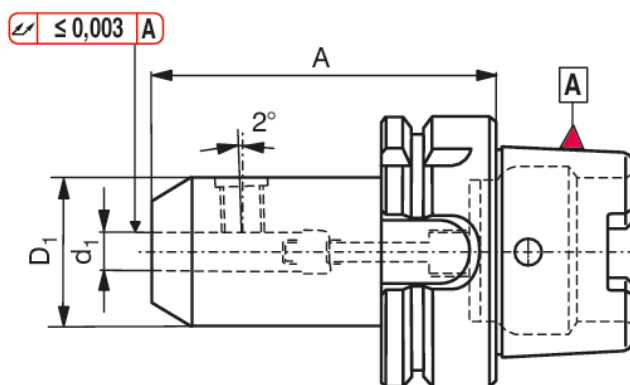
Nástroj s vyfrézovanou drážkou[32]
